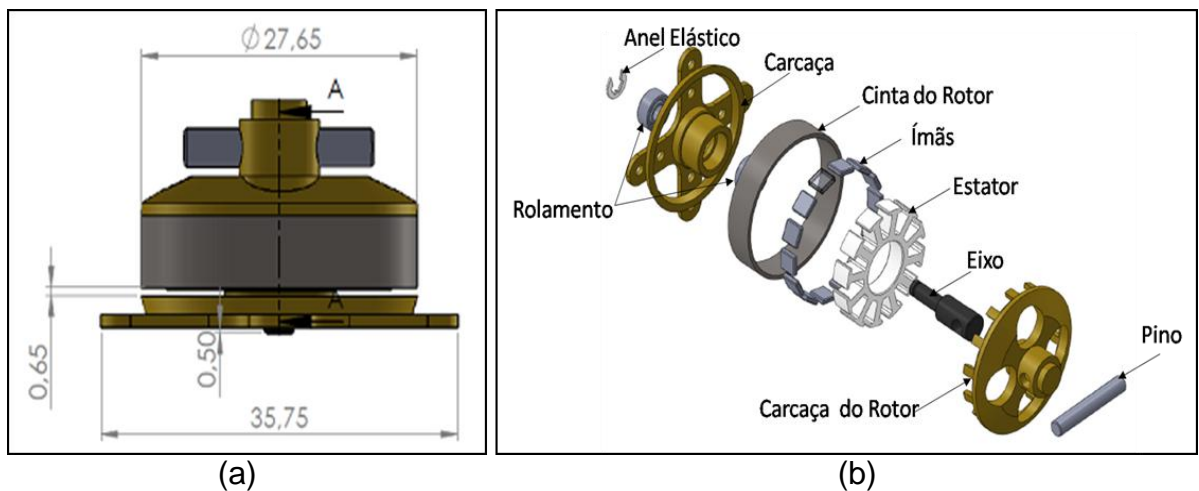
(a) Mini-motor montado – (b) Vista explodida do mini-motor com os componentes.
